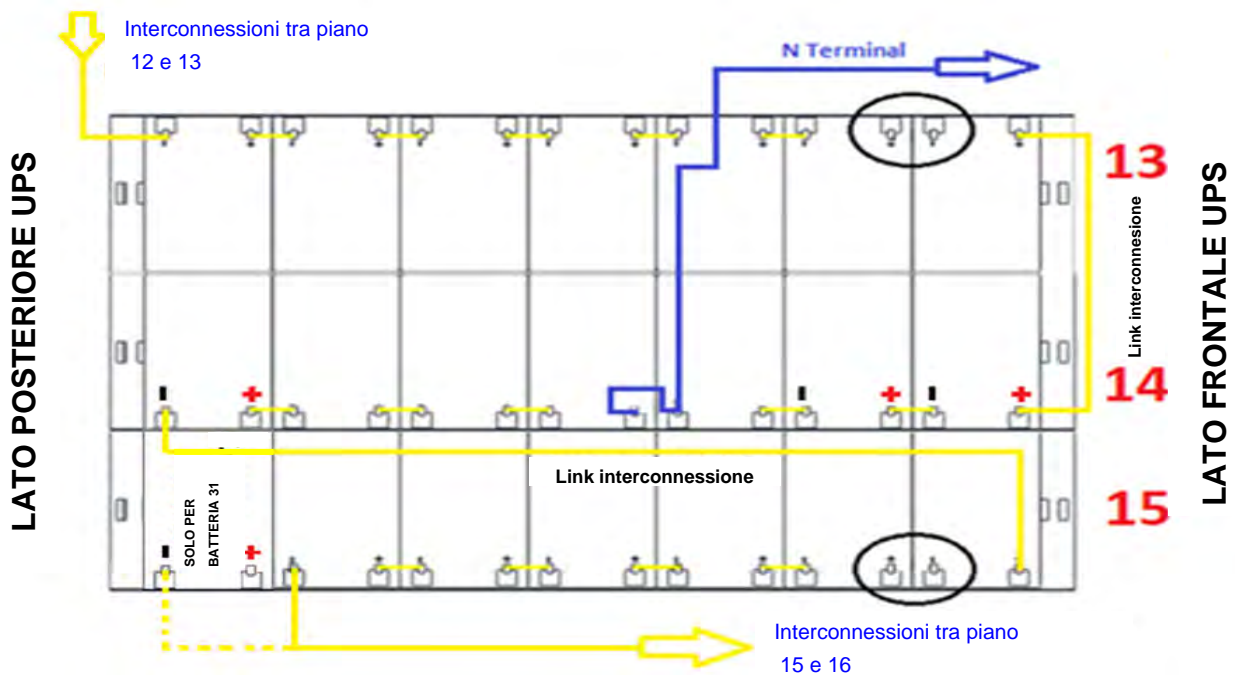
Vista dall'alto Piano N°5 con connessioni batterie
